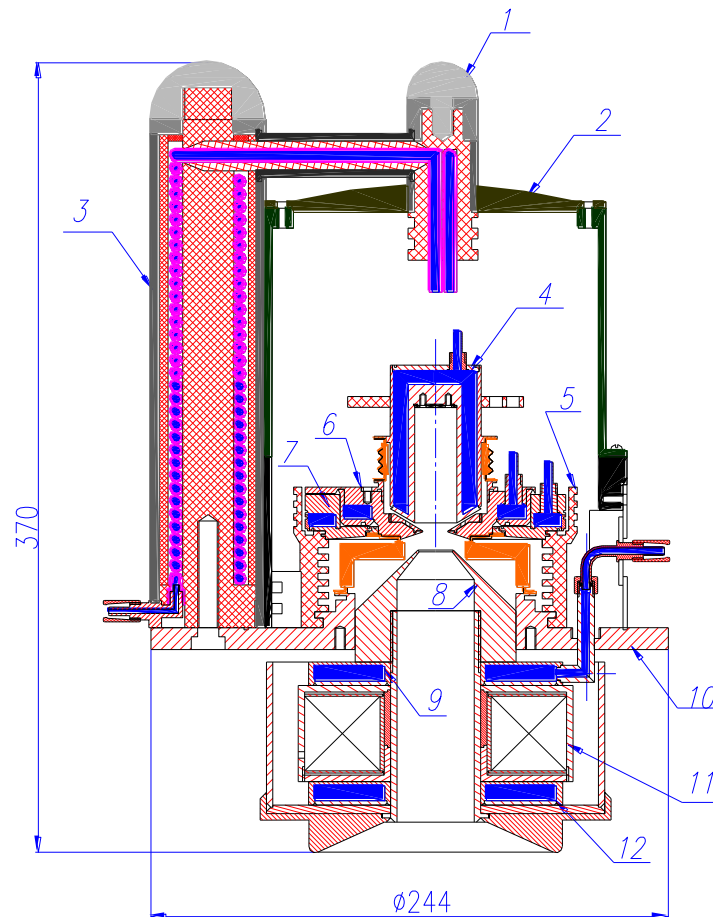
Сборочный чертеж форвакуумного плазменного источника для генерации узкофокусированного непрерывного электронного пучка: 1 – высоковольтный ввод воды; 2 – корпус источника; 3 – водяное сопротивление; 4 – полый катод; 5 – капролоновый фиксатор; 6 – анод; 7 – анодный держатель; 8 – экстрактор; 9, 12 – водяные рубашки охлаждения; 10 – основной фланец; 11 – фокусирующая система [93]
